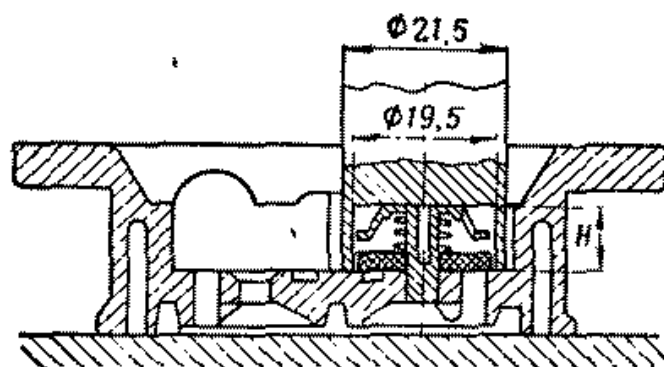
Оправка для запрессовки обойм клапанов топливного насоса:
